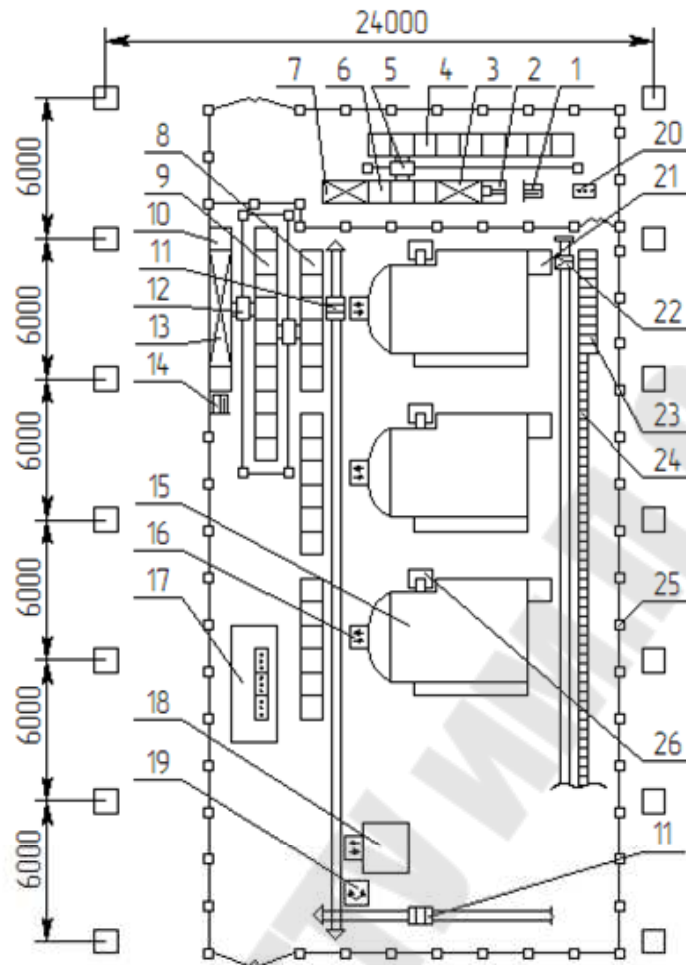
Пример компоновки ГПО для обработки корпусных деталей:
